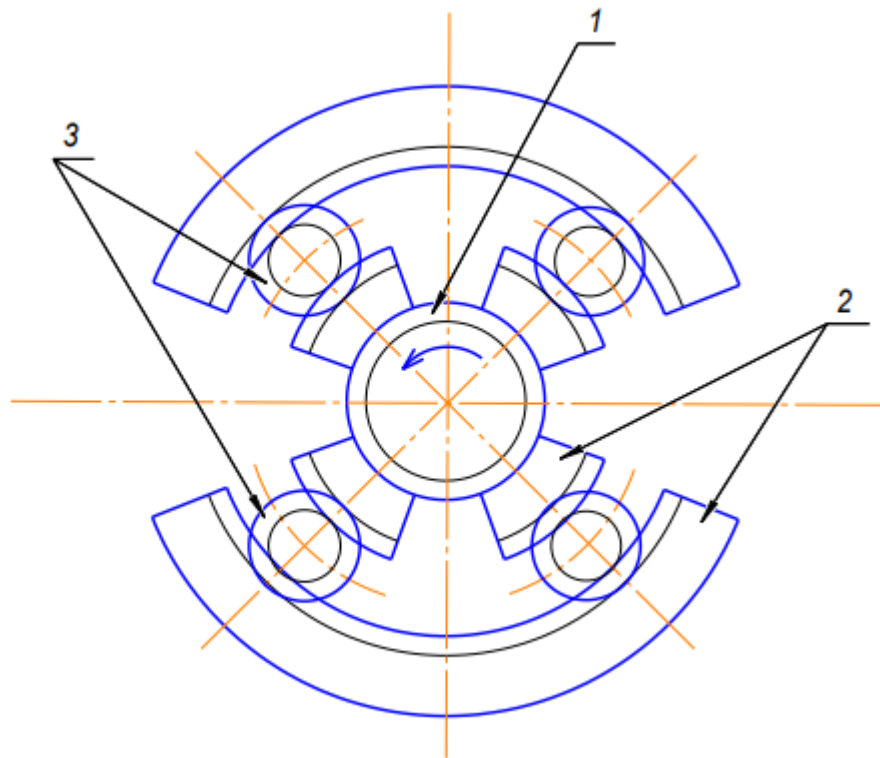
б – Планетарний процес накатування: 1 – обертовий нарізевий ролик; 2 – рухливі сегменти; 3 – деталі, що обробляються
